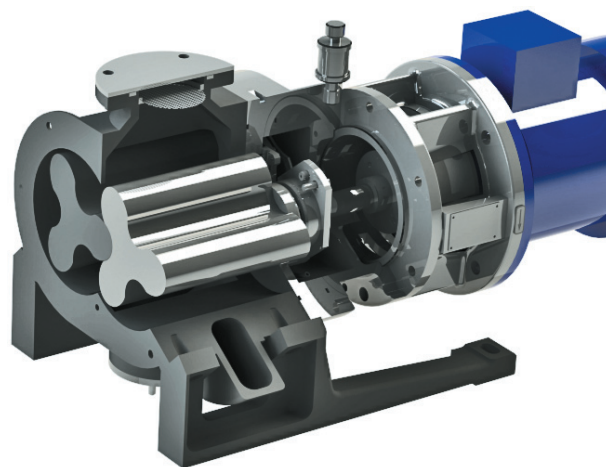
Внешний вид опытного образца ДВН с трехлопастным профилем роторов
